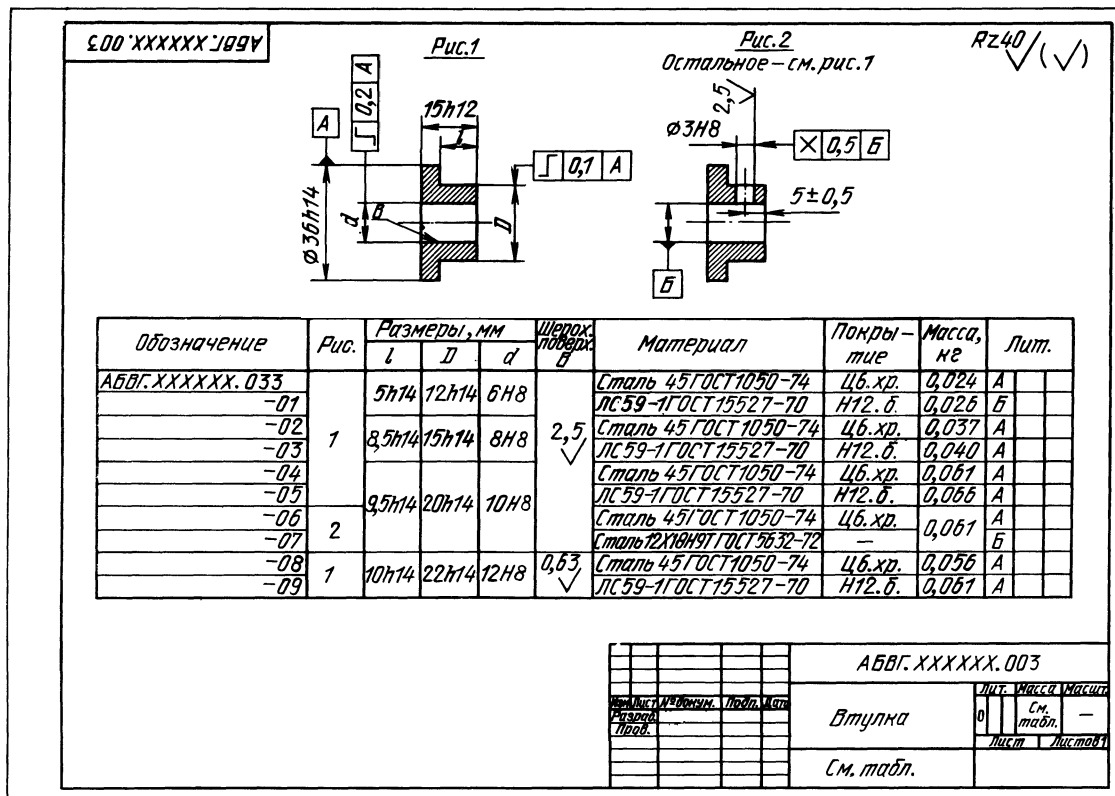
Групповой чертеж деталей с различными параметрами и формами
